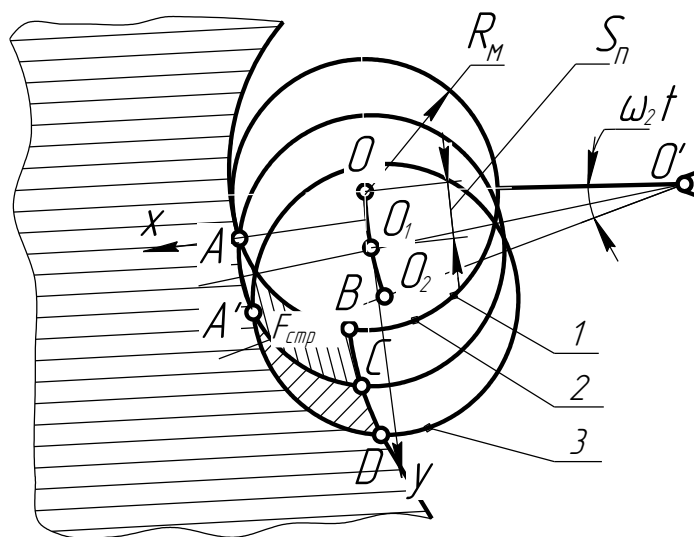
Схема утворення стружки при вільному фрезеруванні:  $R_M$  - траєкторії ножів фрезерного барабана;  $S_n$  – подача барабана» [15].
